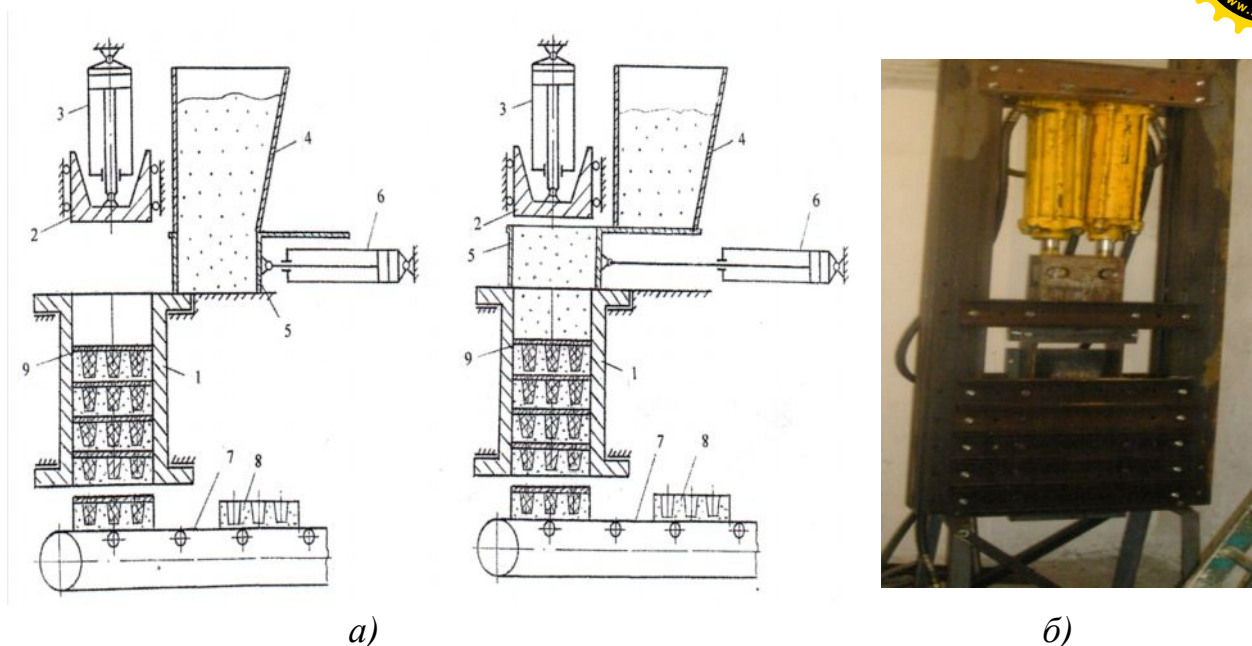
Принципиальная схема и общий вид экструзивного прессового оборудования с движением прессующего пуансона во время формирования изделия вниз
